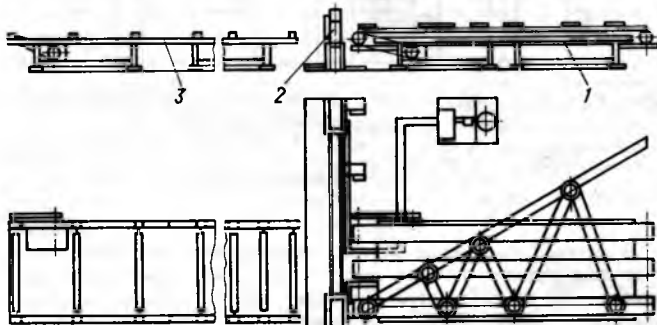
Схема установки для сборки полуферм и ферм с применением металлических зубчатых пластин: 1 — ленточный конвейер; 2 — гидравлические прессующие головки; 3 — приемный роликовый конвейер
